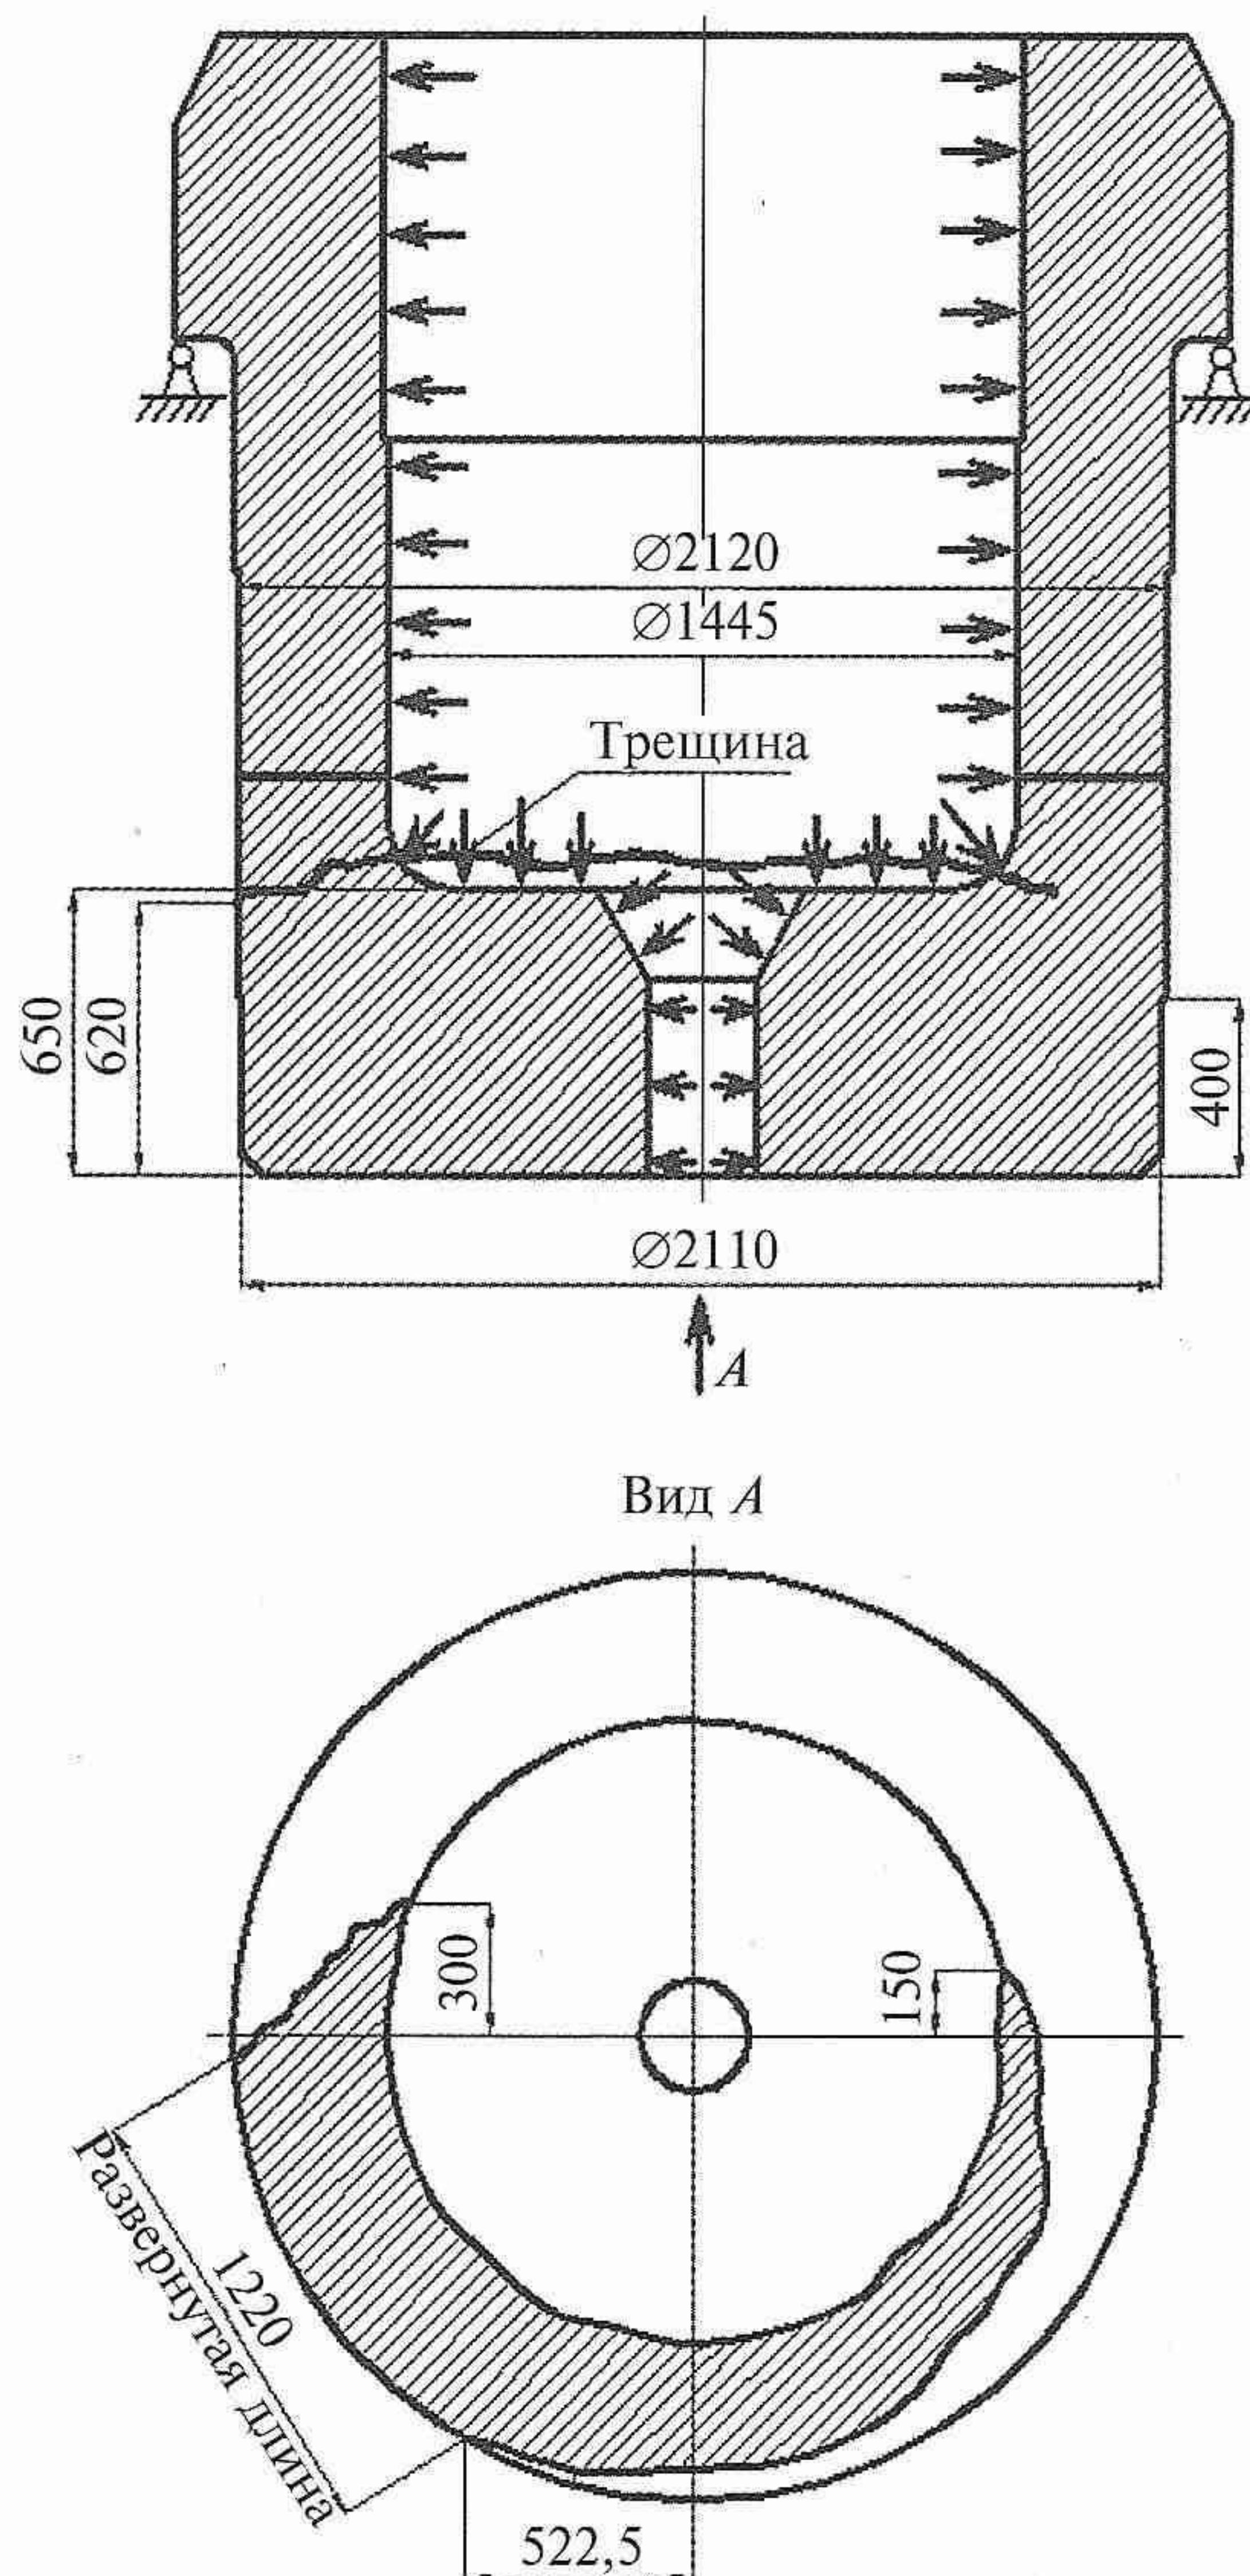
Схема нагружения цилиндра пресса силой 50 МН и размер трещины в днище цилиндра
